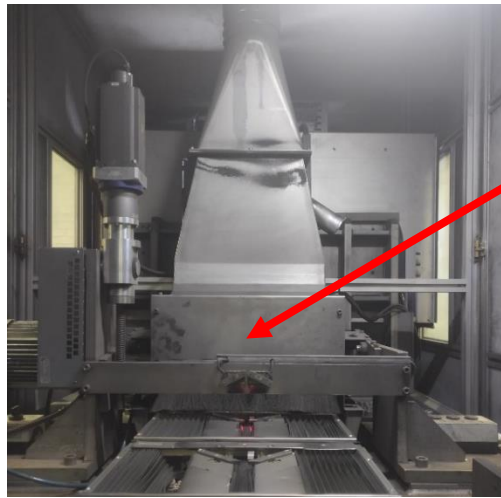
Estación de rectificado plano. Fuente: Elaboración propia
